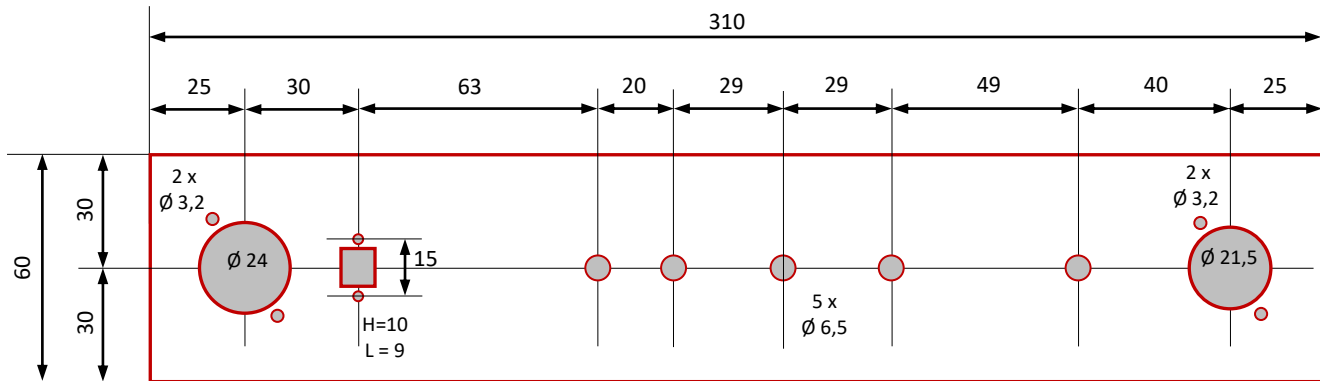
plan de l'usinage de la face arrière – Échelle ½
